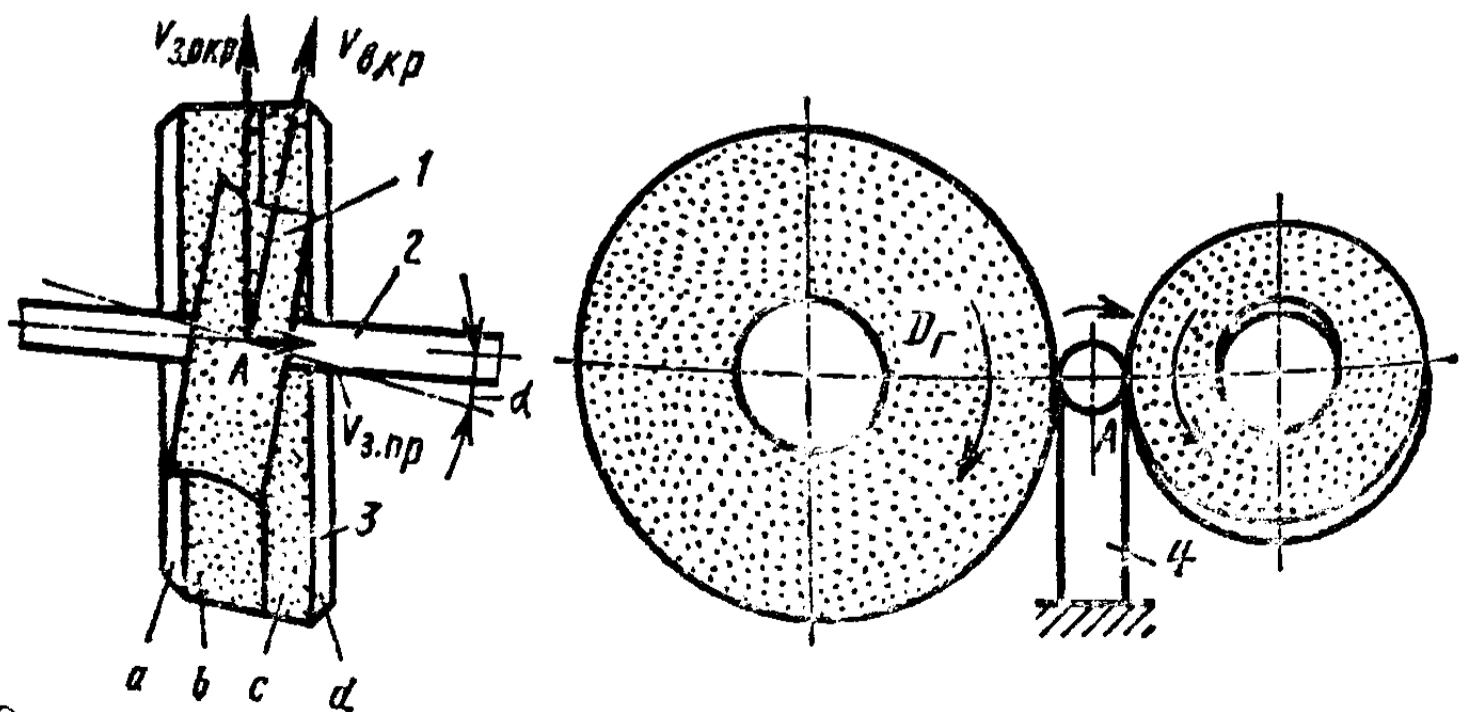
Схема обработки на бесцентрово-шлифовальном станке
